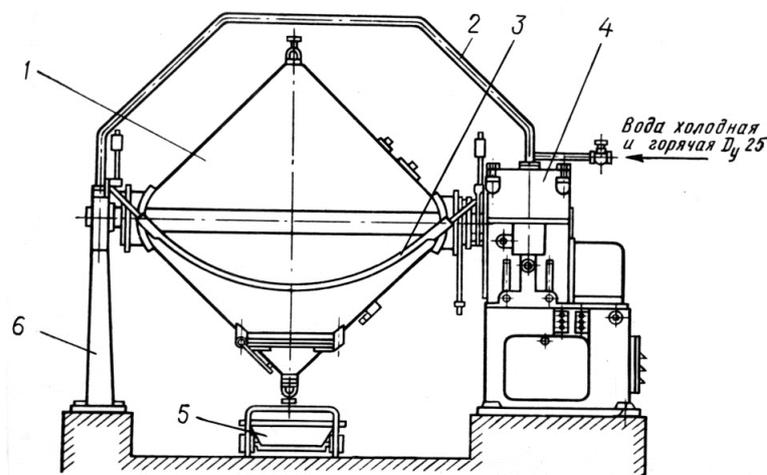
Маслоизготовитель безвальцовый марки РЗ-ОБЭ:
